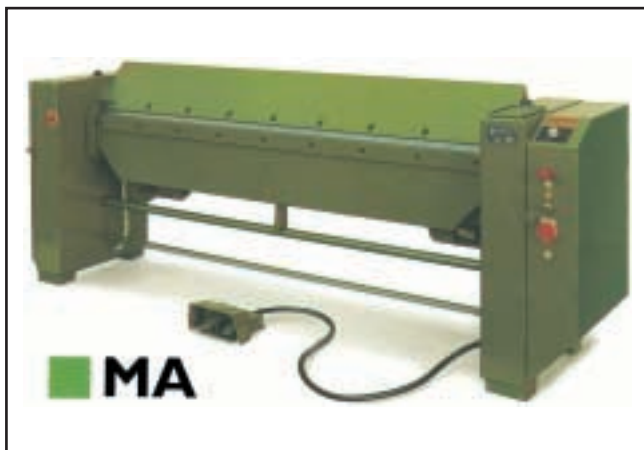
a) - Una macchina MA per piegatura a rotazione (Schechtl/Carbonini)
